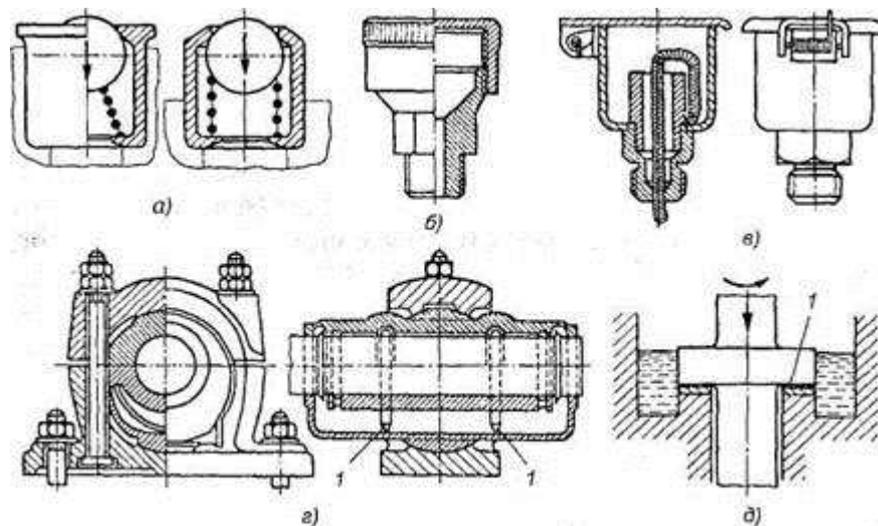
Способы смазывания подшипников: *а* — масленка с шаровым клапаном; *б* — колпачковая масленка; *в* — масленка с фитилем; *г* — смазывание кольцом; *д* — смазывание окунанием
